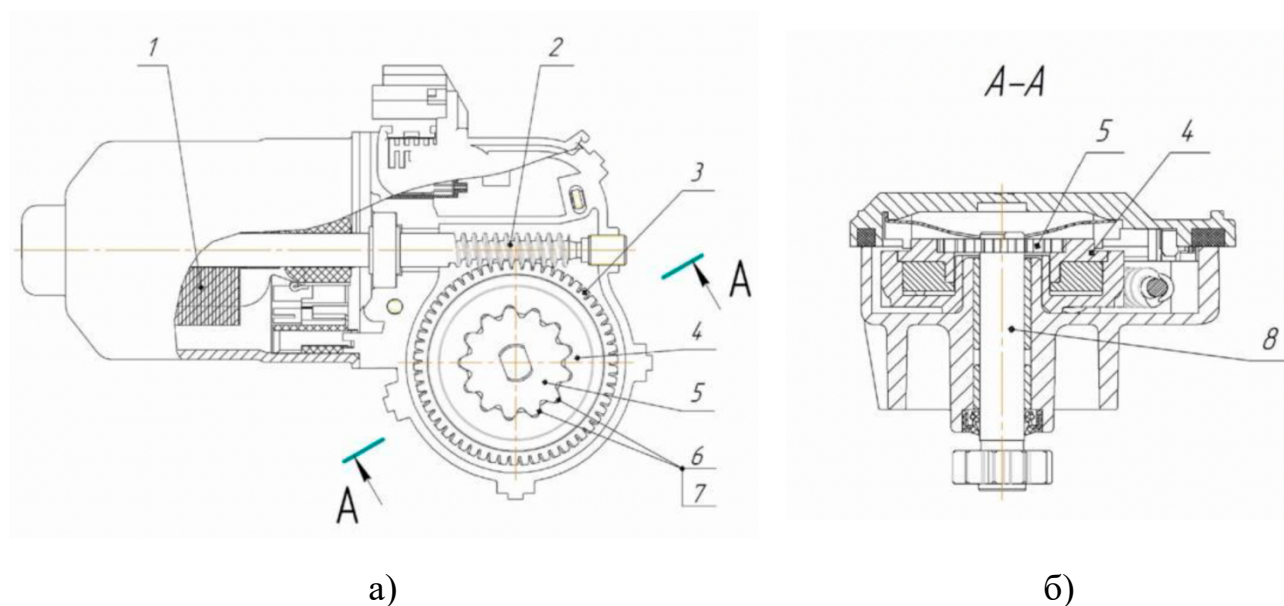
Электромоторедуктор привода двери и подножки: а) общий вид; б) механизм аварийного расцепления
